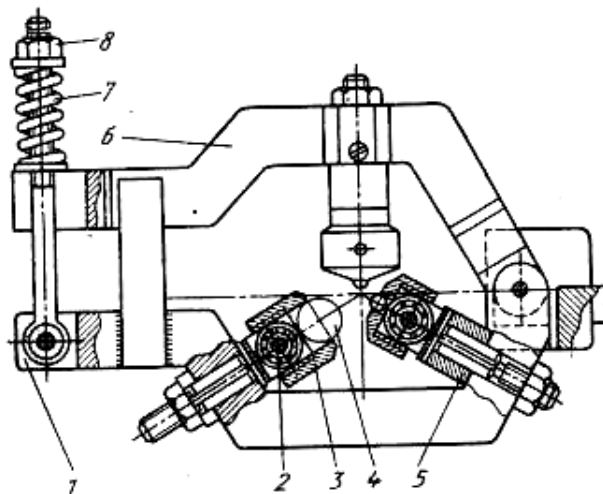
Багатоконтактний інструмент для вигладжування деталей низької жорсткості [30]
